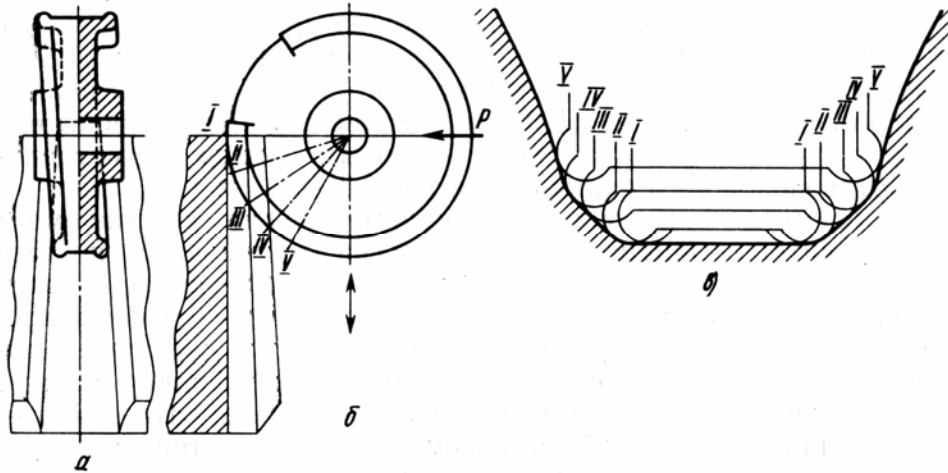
Устройство для поперечного обкатывания зубчатого колеса бортовой передачи экскаватора на токарном станке
